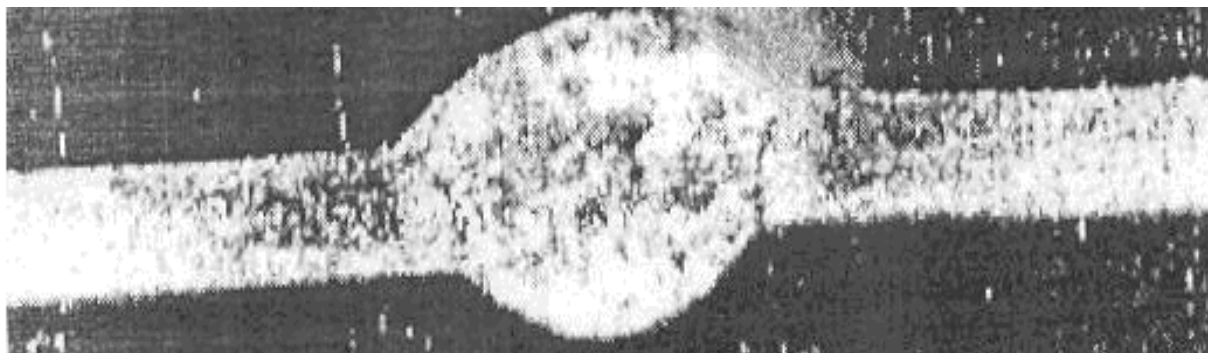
Макроструктура сварного соединения при параметрах сварки
